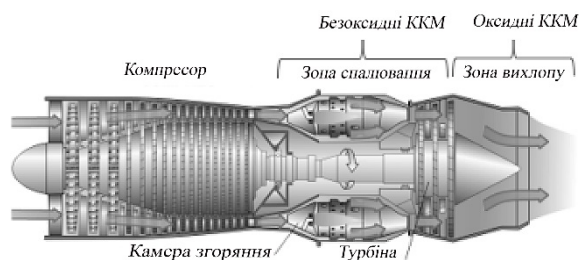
Частини двигуна, що виготовляються із ККМ [83]
